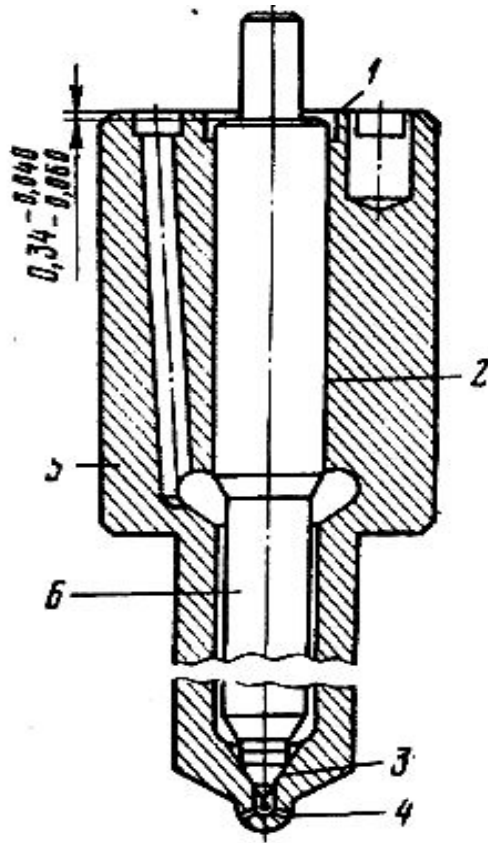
Основні дефекти корпусу розпилювача і голки форсунки двигуна ЯМЗ
